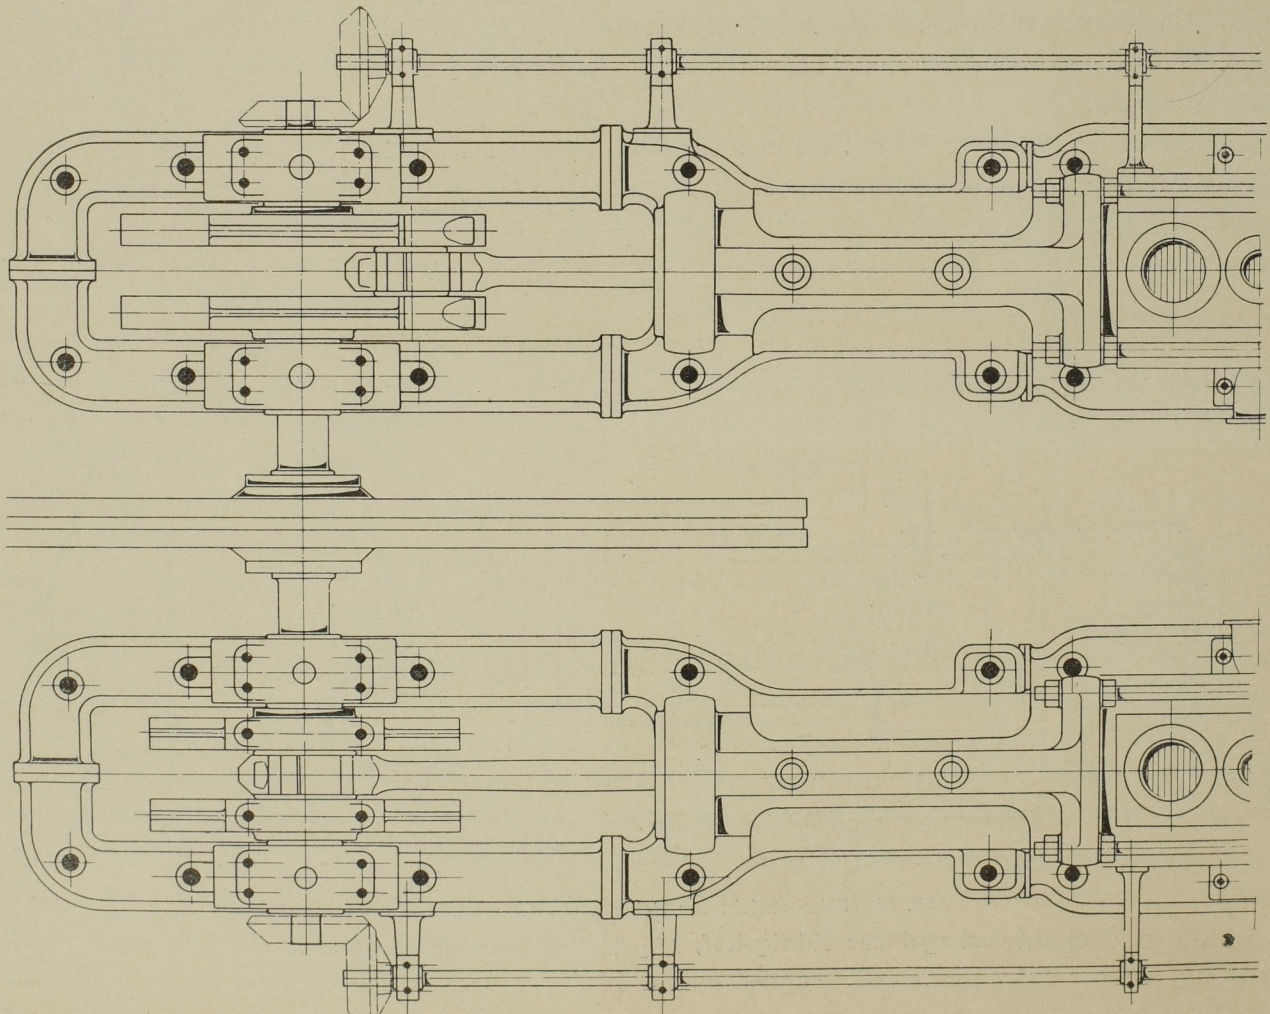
Grundriss des Triebwerks. Masst. 1:50.
